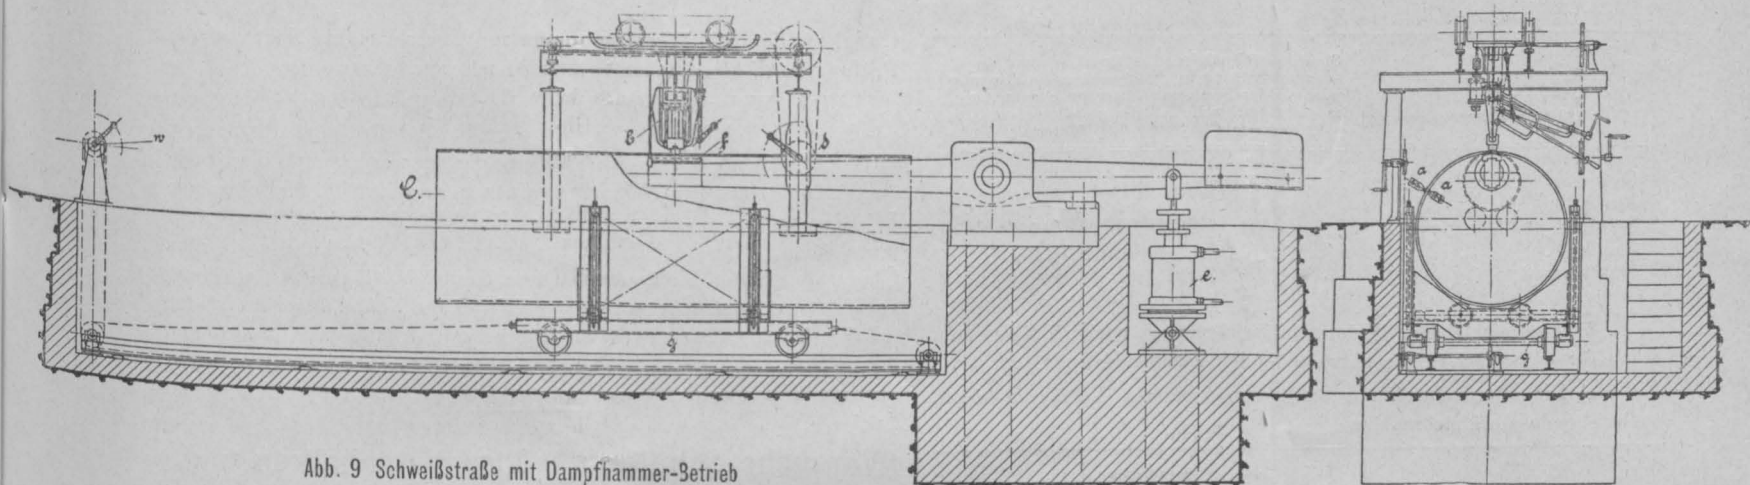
Schweißstraße mit Dampfhammer-Betrieb
